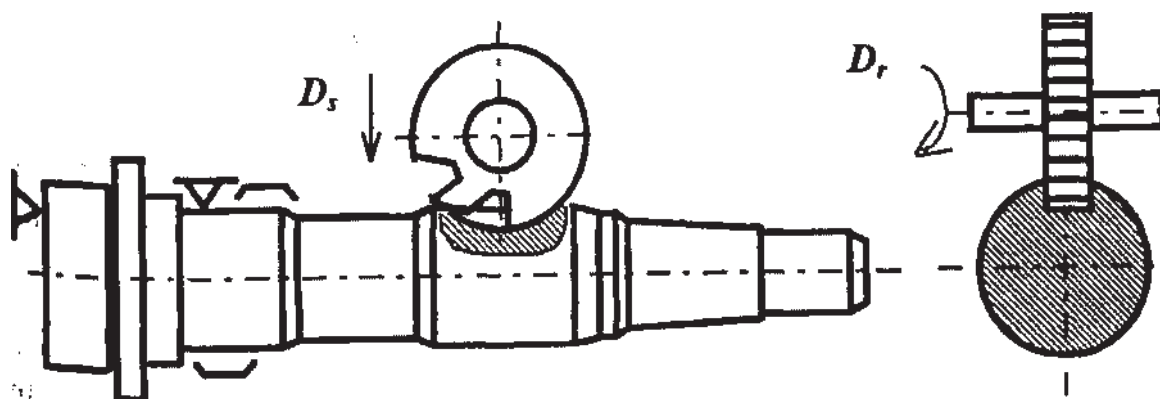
Схема фрезерования паза под сегментную шпонку
